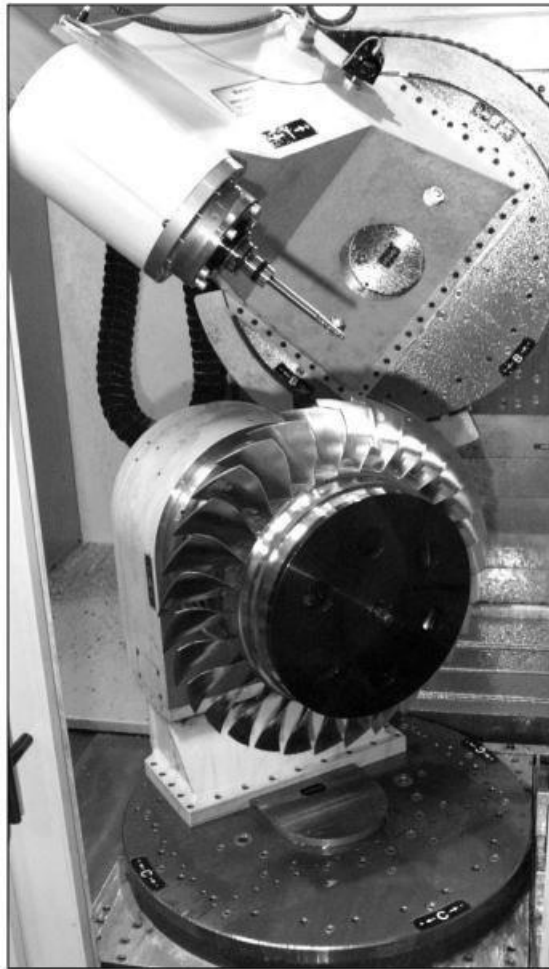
Виготовлення моноколеса на фрезерному станку по типу Turboblisk.
